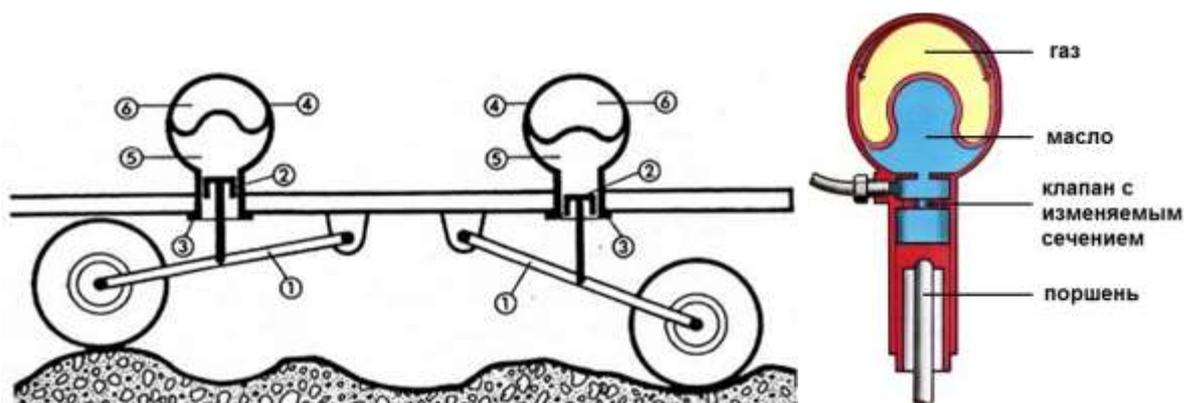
Принципиальная схема гидропневматической подвески: 1 – рычаг подвески; 2 – поршень гидроцилиндра; 3 – корпус гидроцилиндра; 4 – сфера; 5 – масло; 6 – сжатый азот
